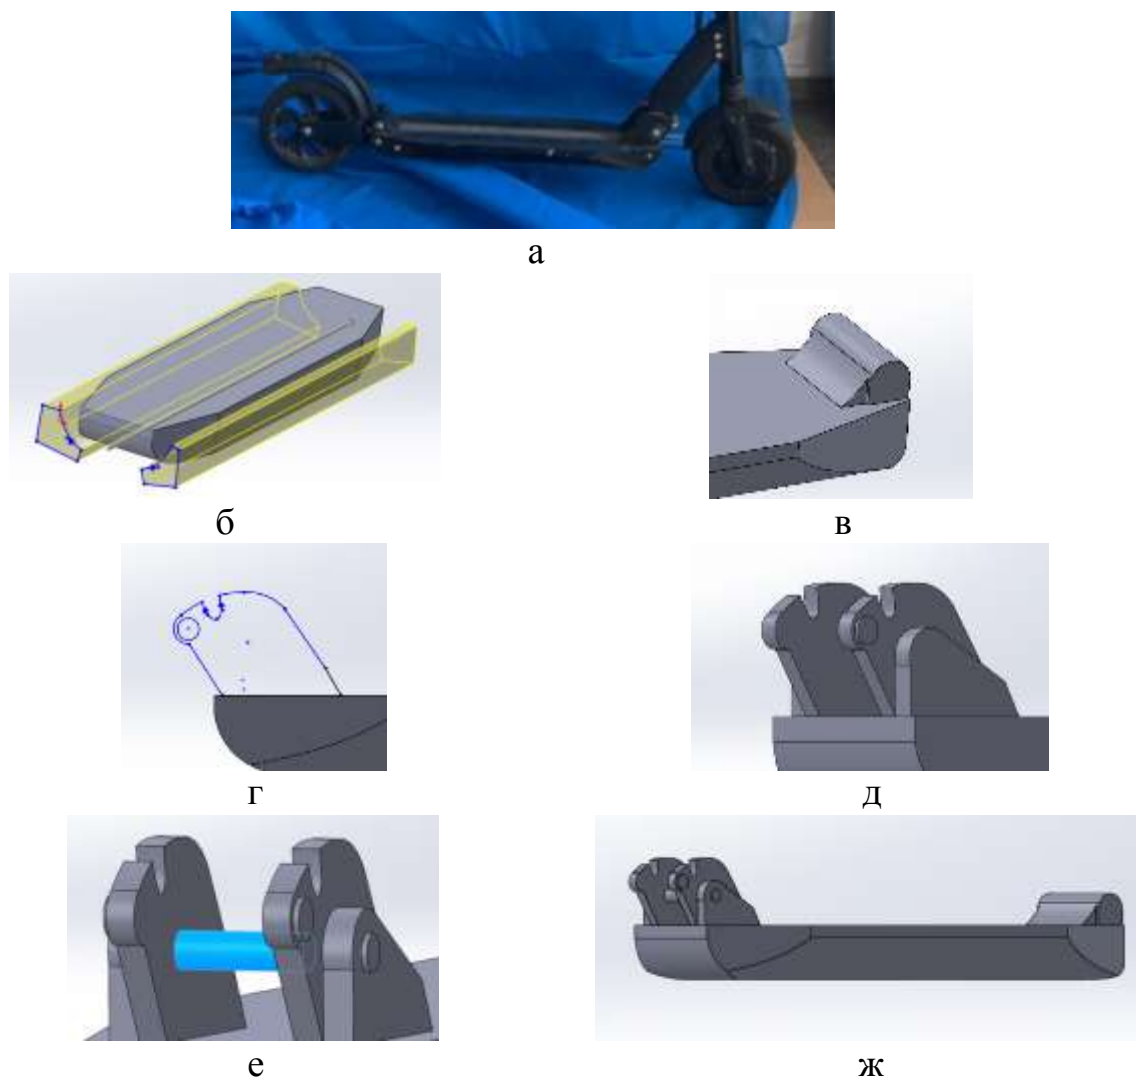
Платформа: а – реальный вид платформы; б – вырез в деке; в – крепление заднего крыла; г – эскиз механизма складывания; д – механизм складывания; е – вал крепления механизма складывания; ж – 3D-модель деки
